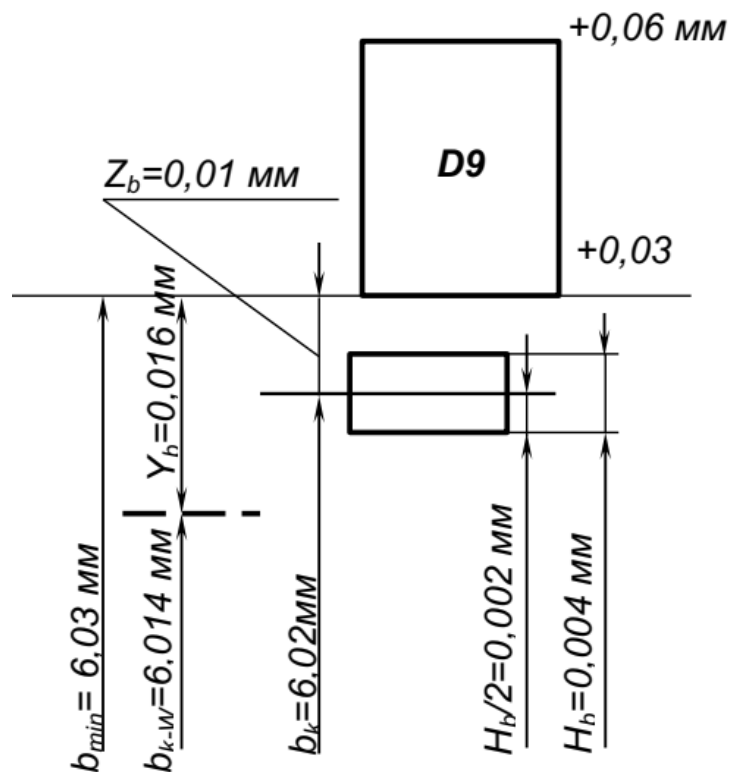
Схема расположения полей допусков комплексного калибр-пробки по ширине шлица
